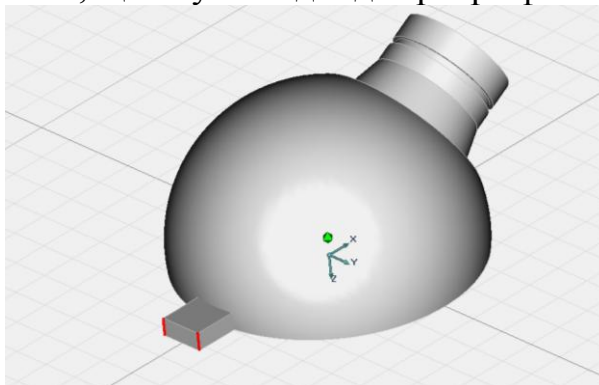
Загальний вигляд двох ребер фланця
